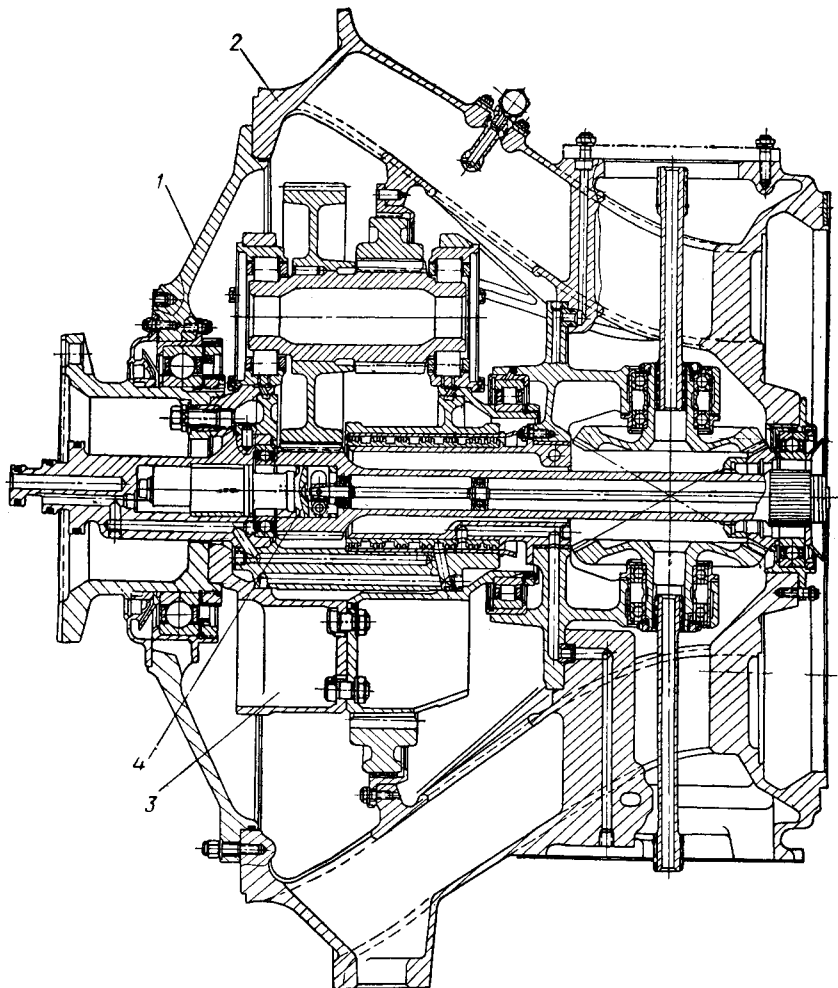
Редуктор ТВД НК-4: 1 – носок редуктора, 2 – картер редуктора с приводами, 3 – ходовая часть редуктора, 4 – механизм измерителя крутящего момента.
